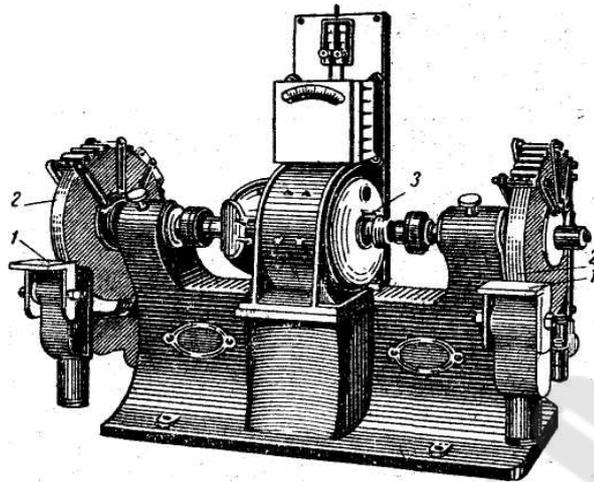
Стационарный шлифовальный станок с двумя камнями: 1- рабочие столики; 2 -шлифовальные круги; 3- электродвигатель
